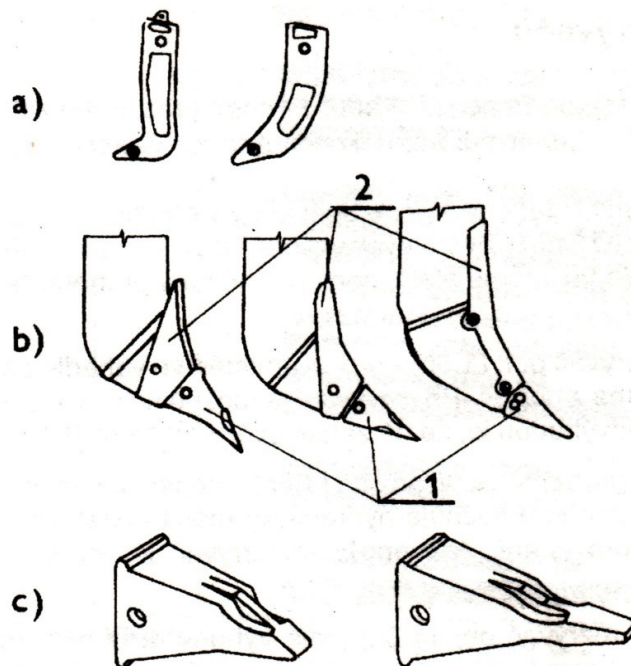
Základní konstrukce návěsných rozrývačů
